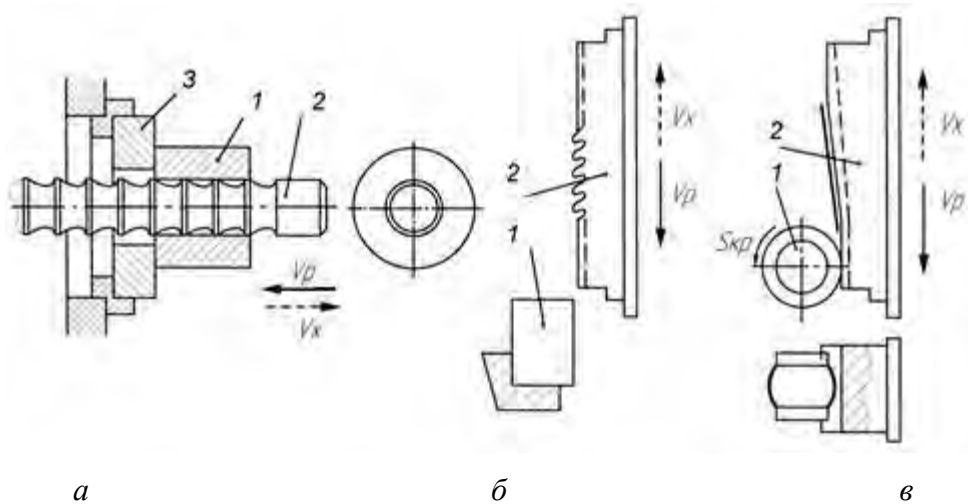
Схемы обработки поверхностей на протяжных станках
